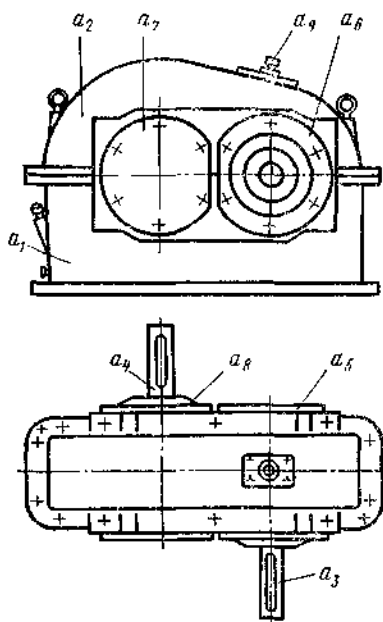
Редуктор цилиндрический: a_1 — корпус редуктора; a_2 — крышка редуктора; a_3 — вал входной; a_4 — вал выходной; a_5, a_7 — крышки глухие; a_8 — крышки сквозные; a_9 — отдушина
